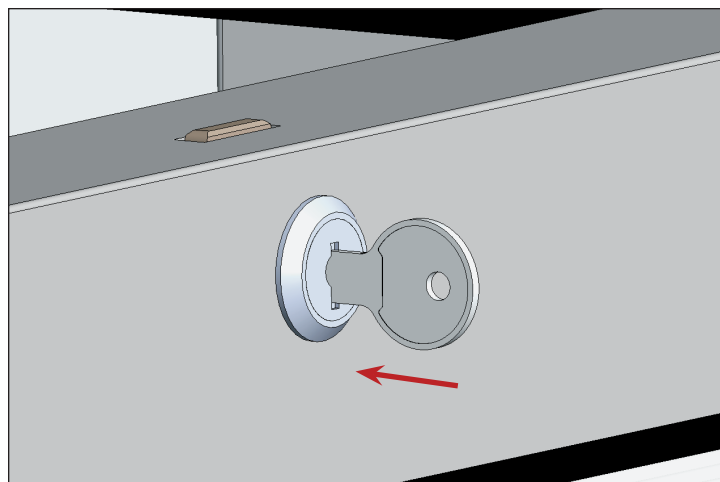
Insérez la clé passe-partout dans le cylindre de la serrure.
